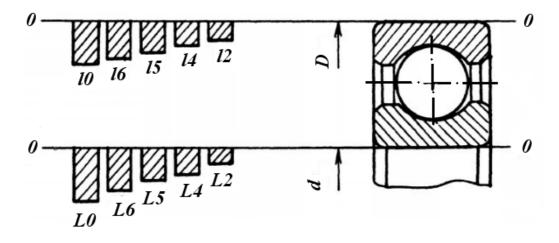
Схема расположения полей допусков наружного и внутреннего колец подшипника качения
